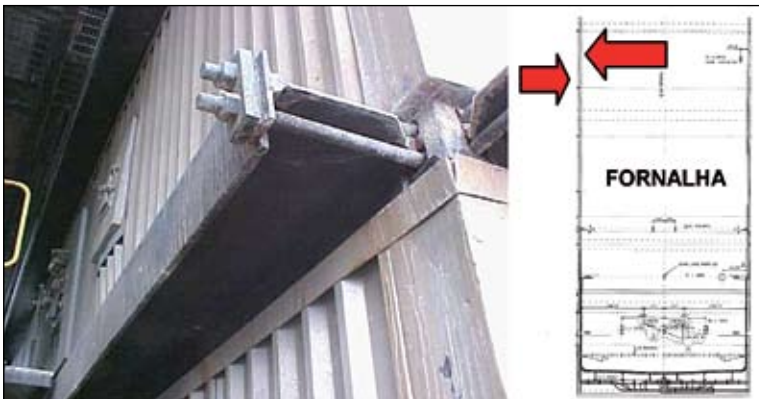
e detalhe auxiliar. Em caso de deformações em paredes de água, as fixações externas dos suportes dos *buckstays* mais próximos devem ser inspecionadas / Figure 8 and auxiliary detail. In case of water wall deformations, the outside fastenings of the supports of the nearest *buckstays* should be inspected
